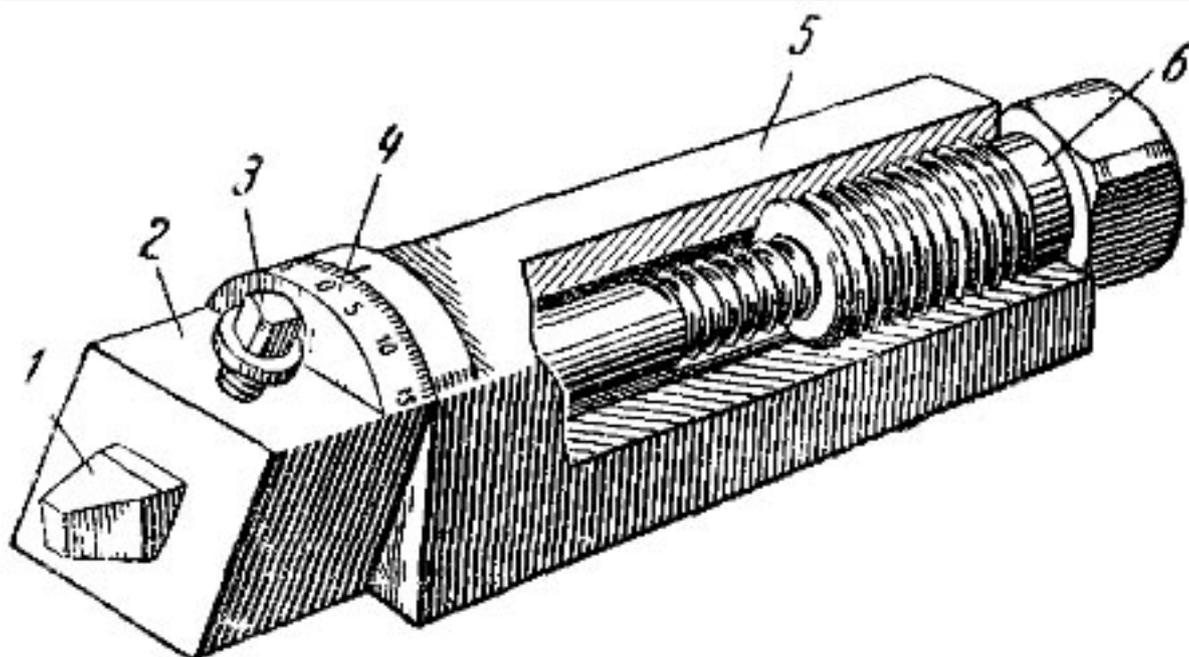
Державка для установки и закрепления резца для нарезания прямоугольной и трапецеидальной резьб
